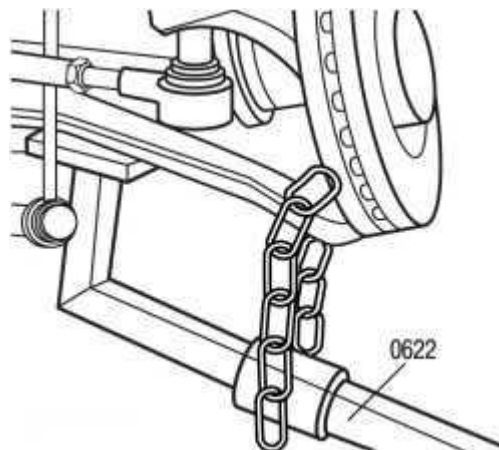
Застосування важеля “0622” для роз'єднання кульових опор з поворотною цапфою
